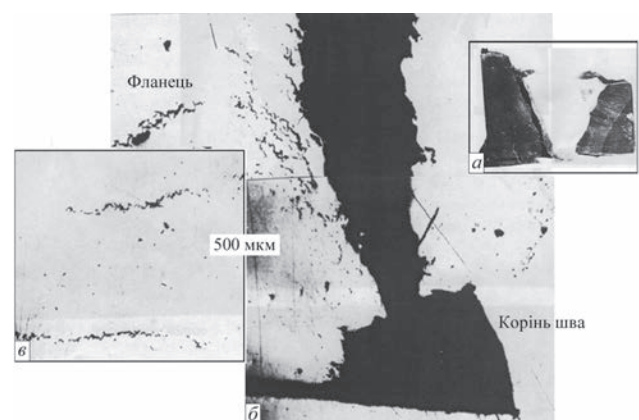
Область руйнування зварного шва приварювання фланця до труби: а – макроструктура; б – магістральна тріщина; в – зигзагоподібні ланцюжки в металі фланця зі сталі 20
